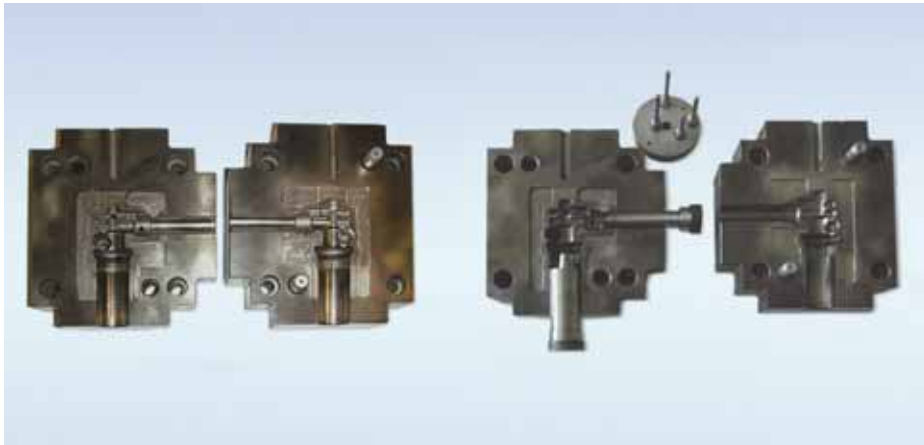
Werkzeugkomponenten für das seitliche Hohlpressen.
